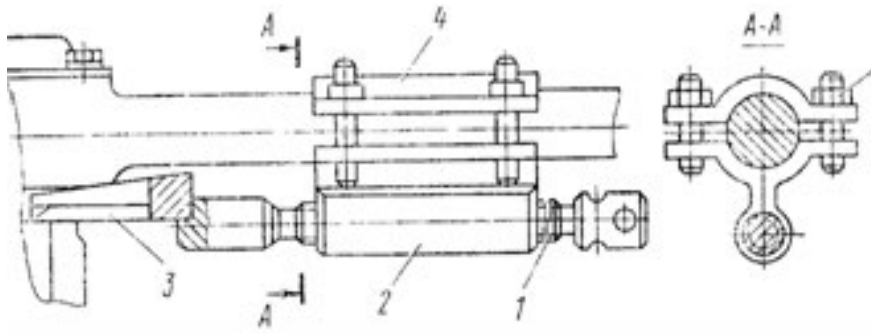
Зняття знімачом пальців реактивних штанг: 1-гвинт; 2 – корпус; 3 – клин; 4 – кришка; 5 – гайка; 6 – шпилька
